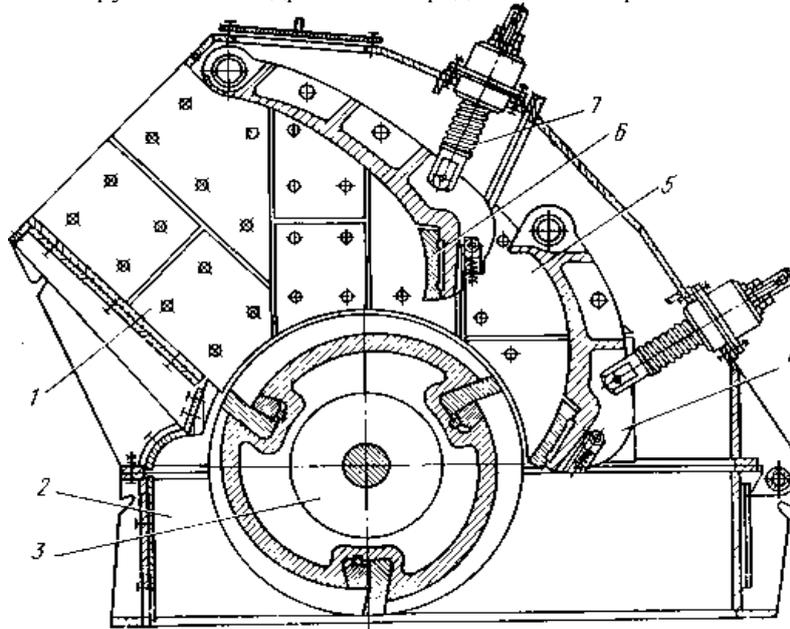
Конструкция роторной дробилки крупного типа дробления
